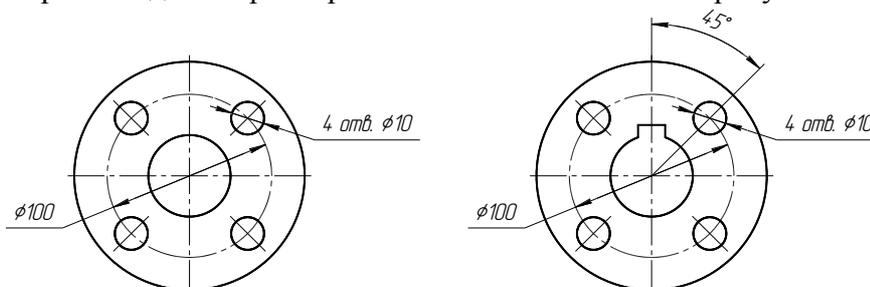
Нанесение размеров на равномерное расположение одинаковых отверстий у симметричных и несимметричных деталей
